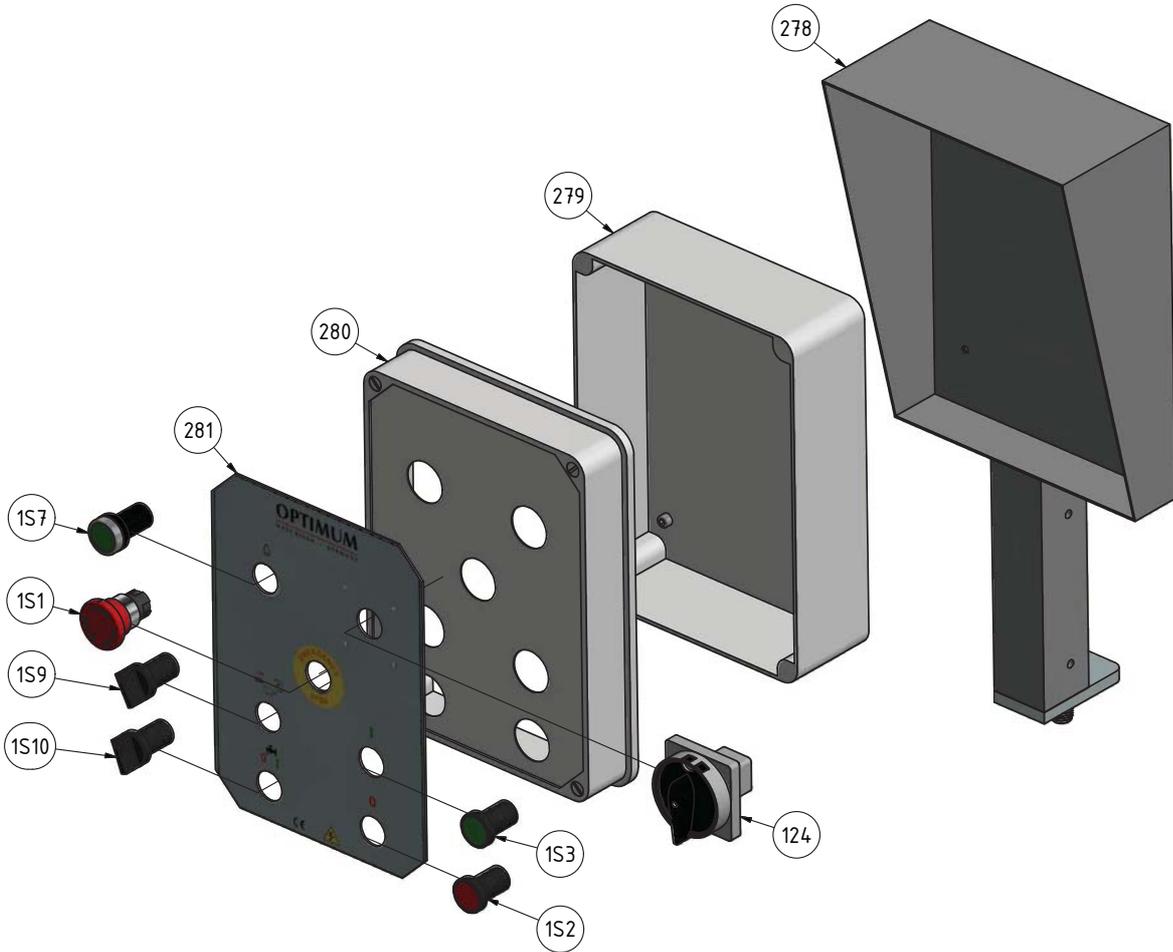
Explosionszeichnung - Drawing spare parts
